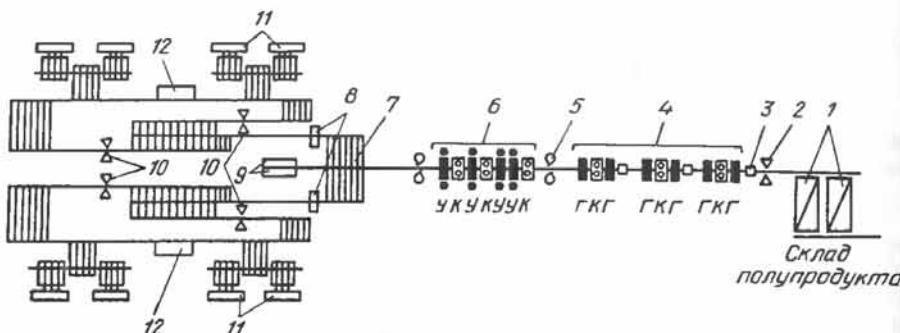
Схема расположения оборудования непрерывного среднесортного стана 450:
